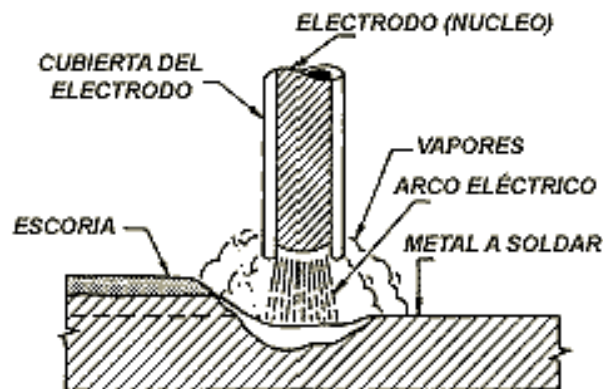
13. Soldadura por arco con electrodo revestido.
